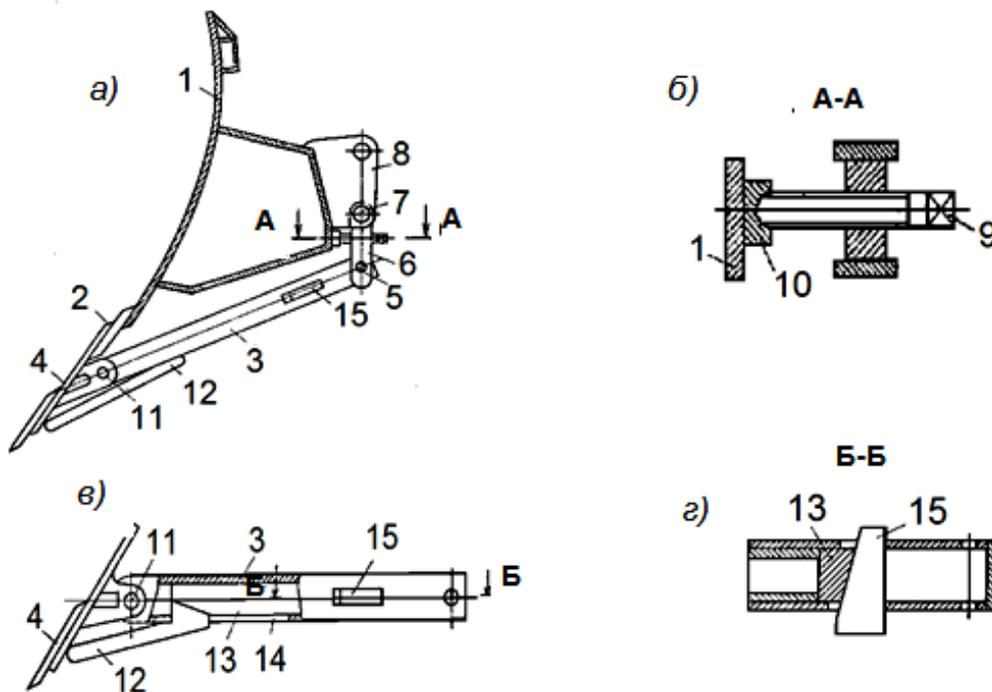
Бульдозерное оборудование в разрезе (а), разрез А-А (б), кронштейн с дополнительным средним ножом (в), разрез Б-Б (г): 1 - отвал бульдозера; 2 - нож; 3 - кронштейн; 4 - дополнительный нож; 5 - шарнир; 6 - рычаг; 7 - палец; 8 - проушина; 9 - болт; 10 - подпятник; 11 - шарнир; 12 - упорный рычаг; 13 - ползун; 14 - пазы; 15 - натяжной клин
